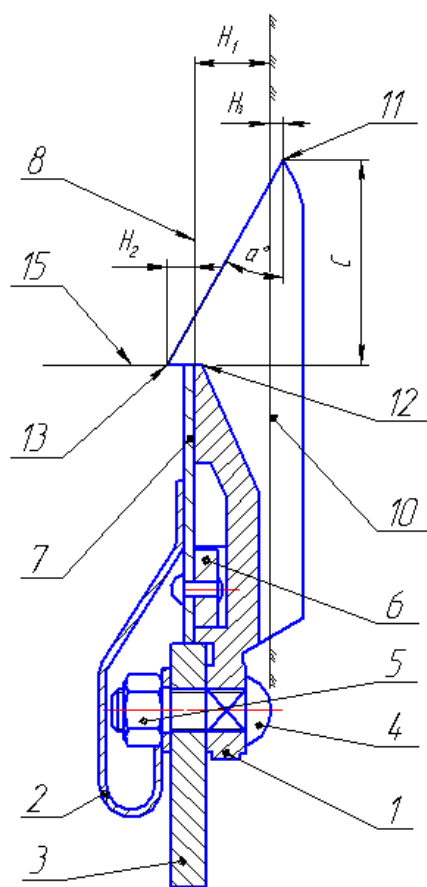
Аппарат режущий жатвенной машины (вид сбоку)
